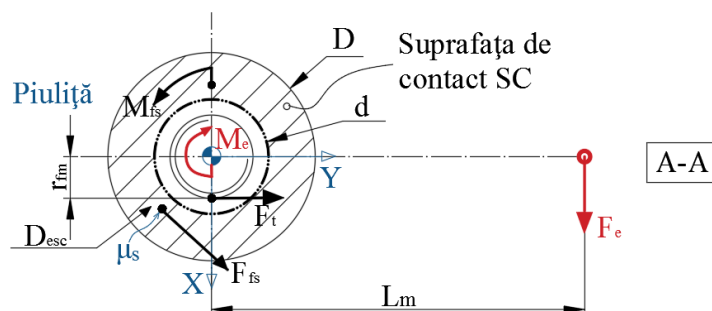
Mecanism de fixare cu piuliță cu guler plat – Secțiunea A-A
